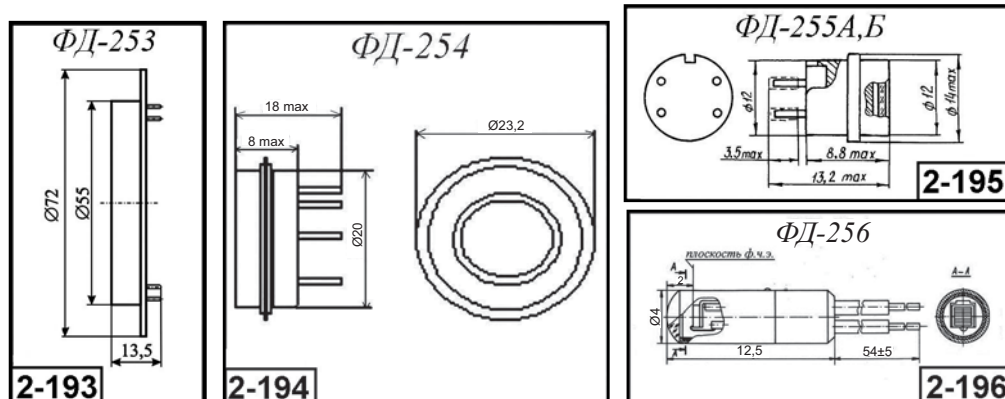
Внешний вид, габаритные размеры кремниевых фотодиодов
